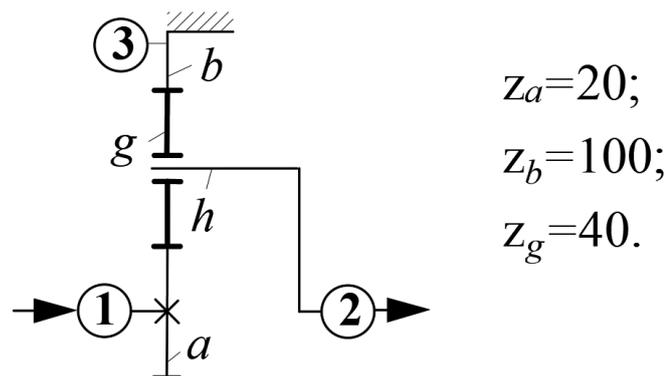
Схема планетарного механизма с однозвеновым сателлитом
